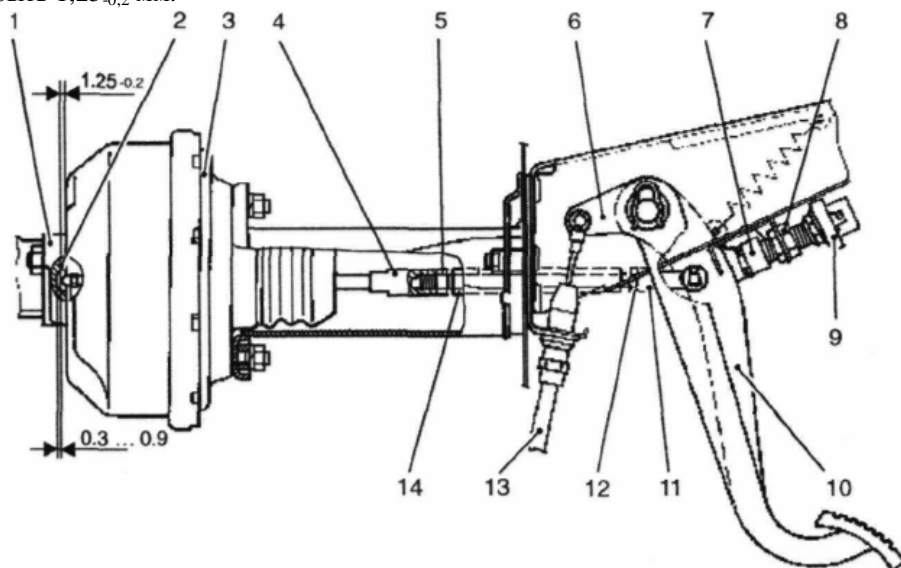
Педаль и привод ножного тормоза с вакуумным усилителем:
